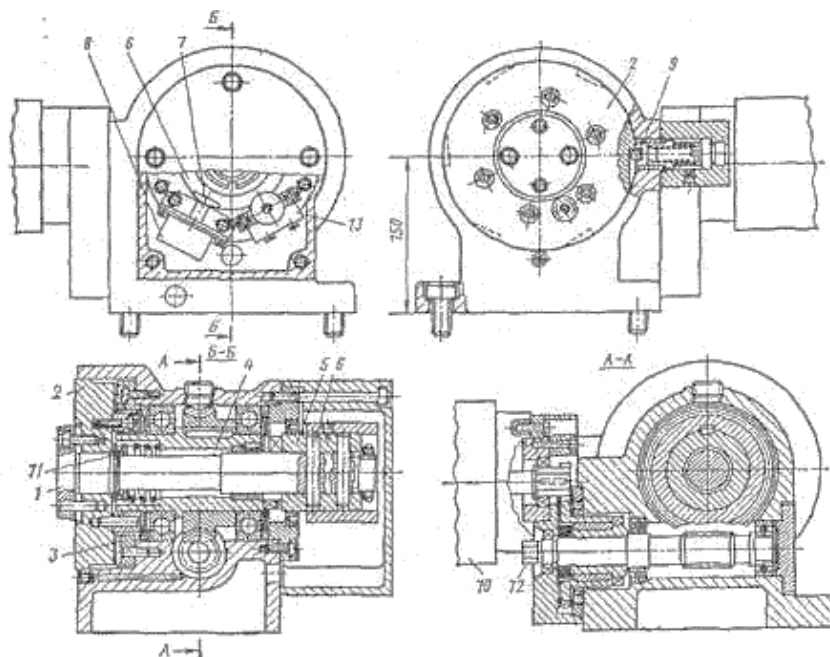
Поворотний різцетримач токарно-гвинторізного верстата
